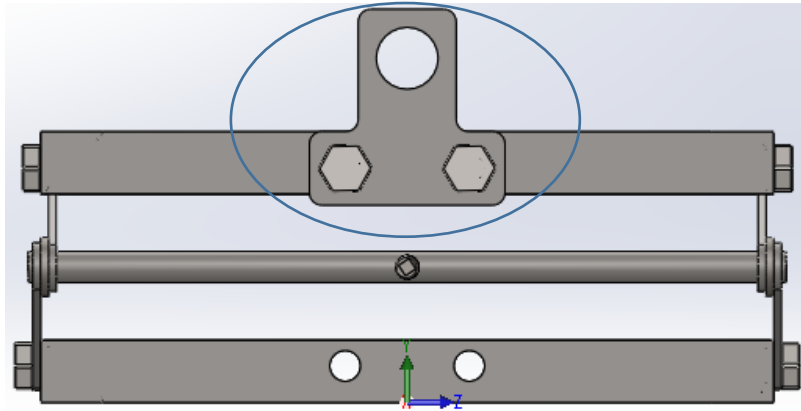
Ubicación de la placa de conexión en el Sistema de Elevación.
